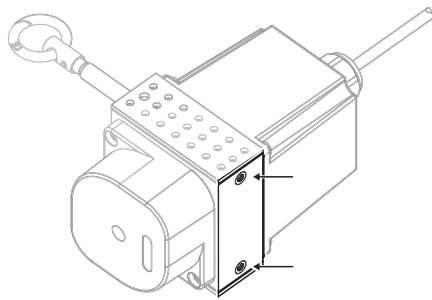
Befestigungsbohrungen DWE-...-60-...
